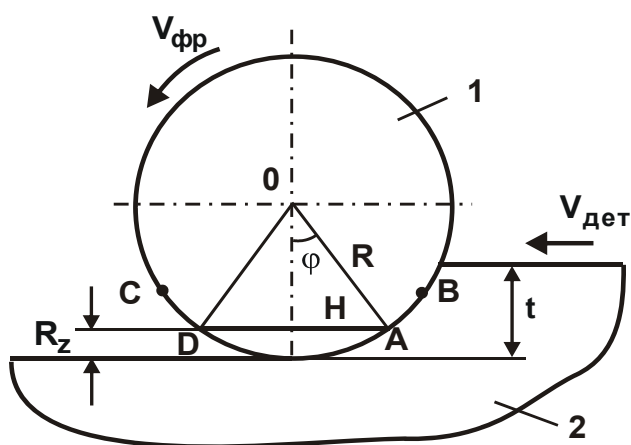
Расчетная схема параметров фрезерования цилиндрической фрезой:
